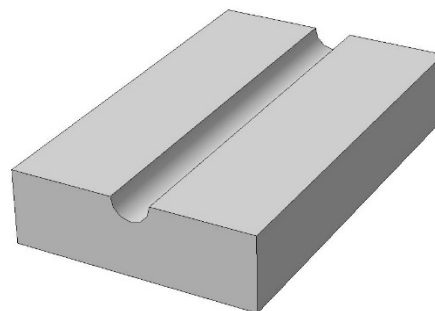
Оснащення для шліфування бічної поверхні багатогранної заготовки.
